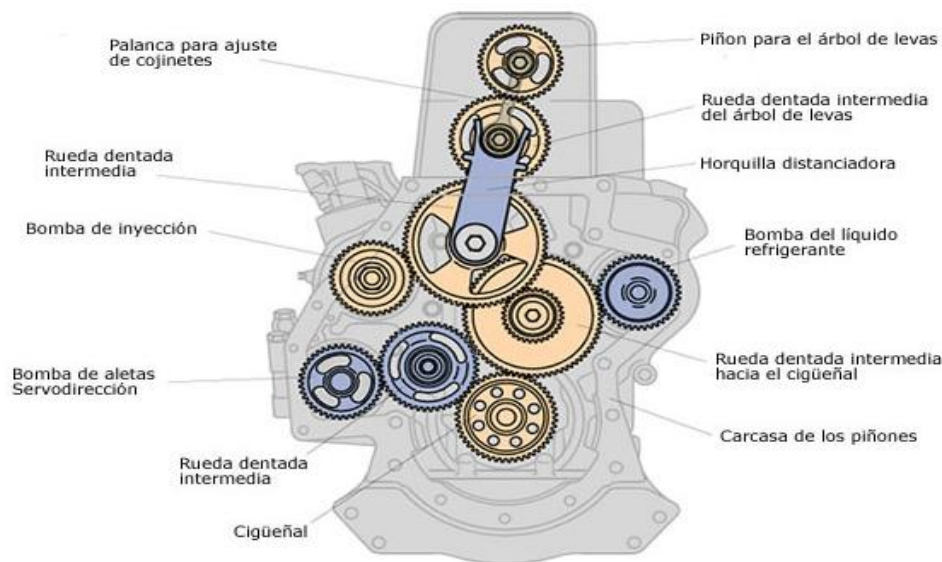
Engranajes de Distribución del Motor. (Caterpillar, 2015)
